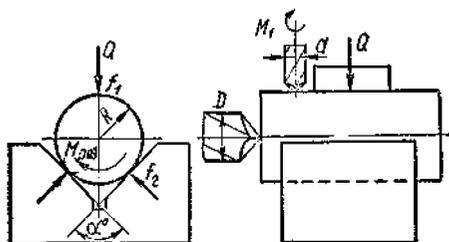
Схема установки детали в призму и расположения сил при сверлении
